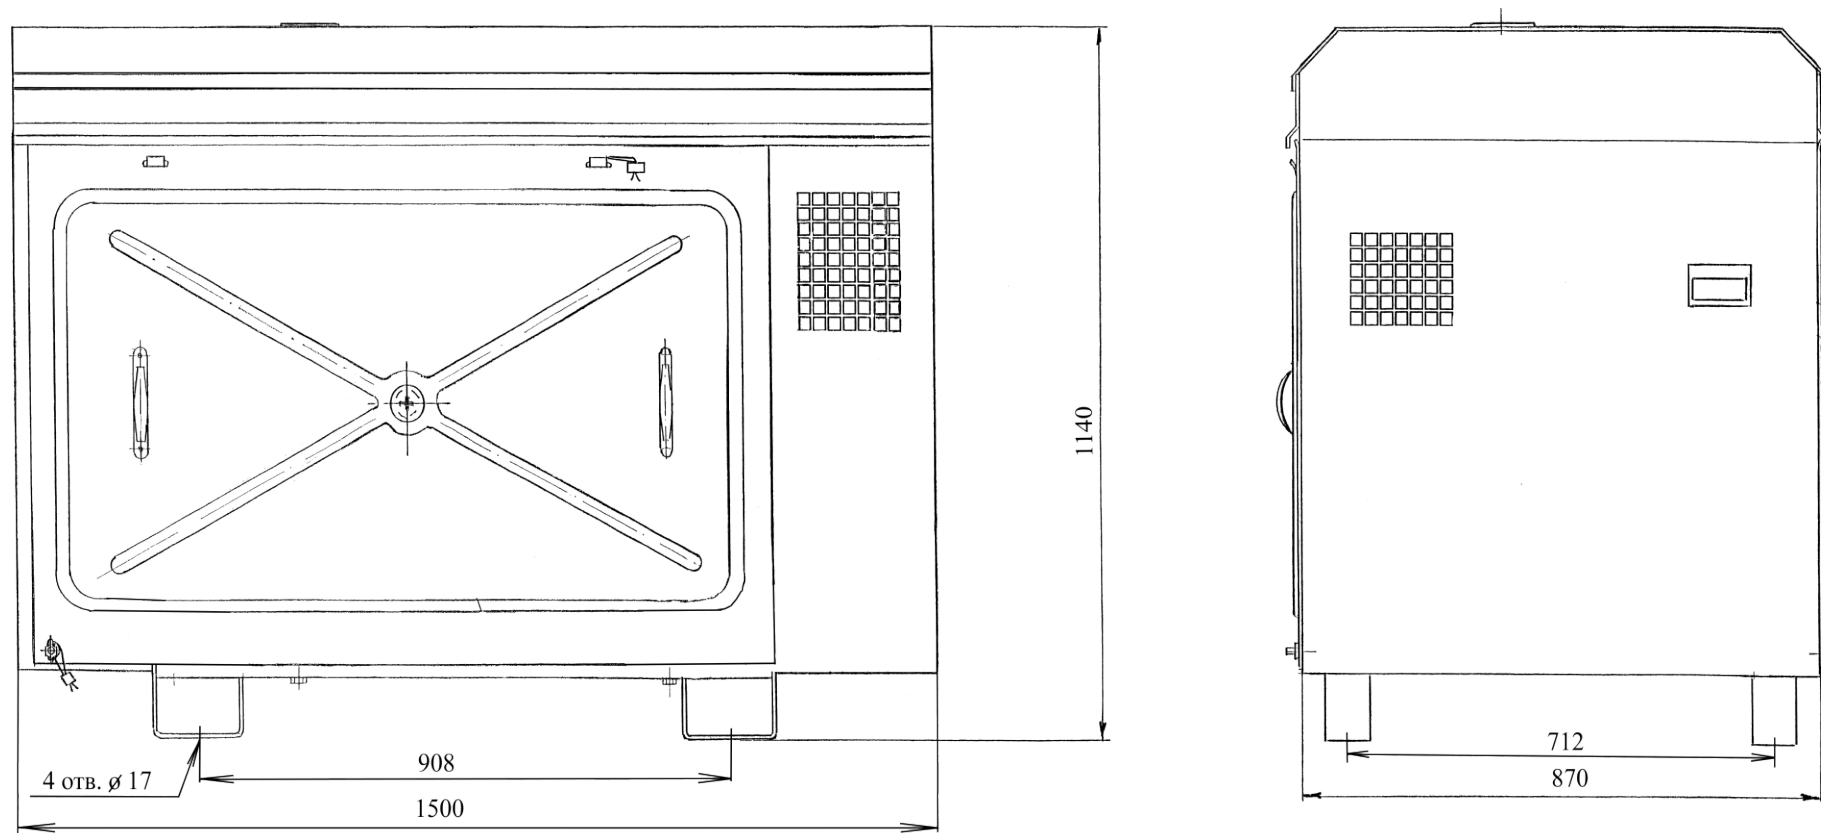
Габаритный чертеж компрессорных станций ЗИФ-СВЭЗ/0,7 (АРМ19-22-01)
